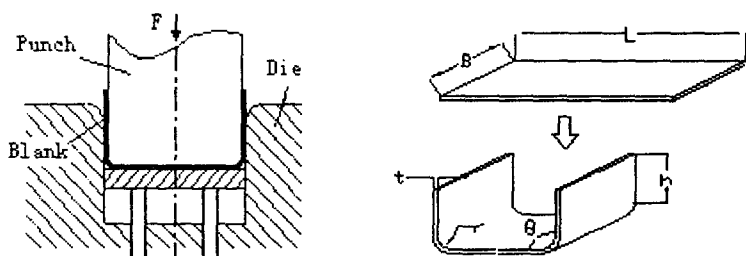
U 形弯曲模具结构和试验毛坯及工件参数
